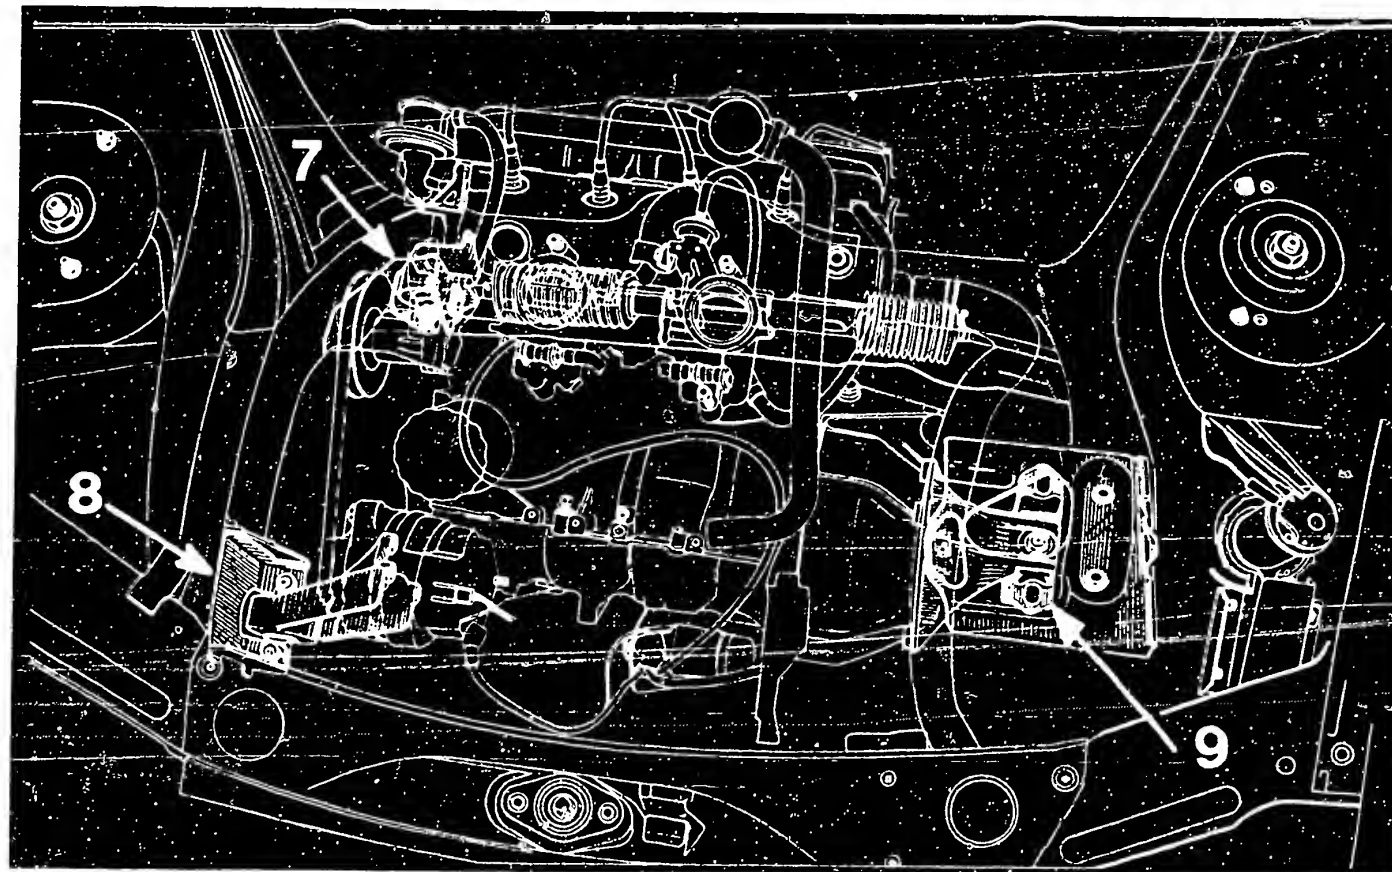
Lage der Motoraufhängungen. 7 hinten – 8 vorne rechts – 9 vorne links.
